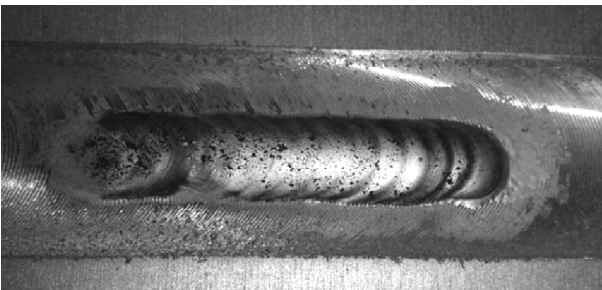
Внешний вид шва СТП сплава 1565ч после наложения подварочного шва аргонодуговой сваркой
